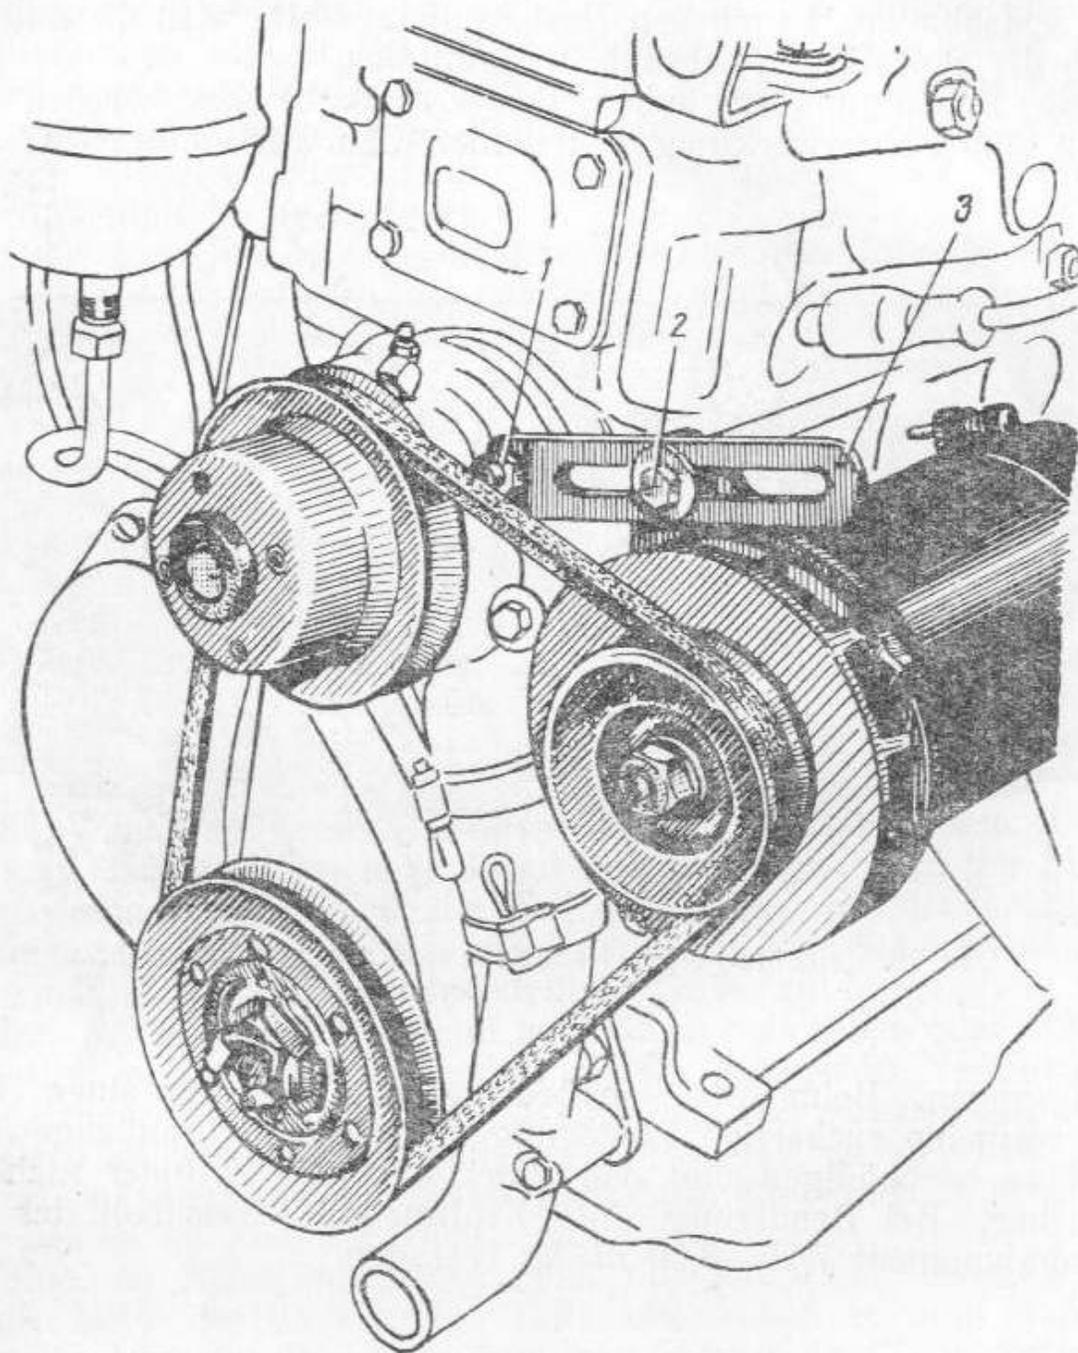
Anordnung und Befestigung der Lichtmaschine am Motor
